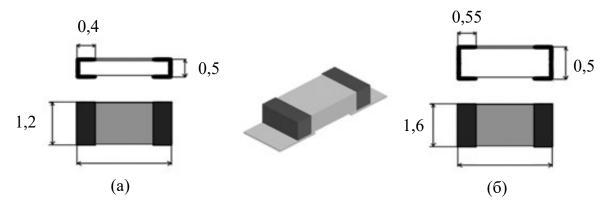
Габариты чип компонентов (мм) – типоразмера 0805 под (а) и типоразмера 1206 под (б)
